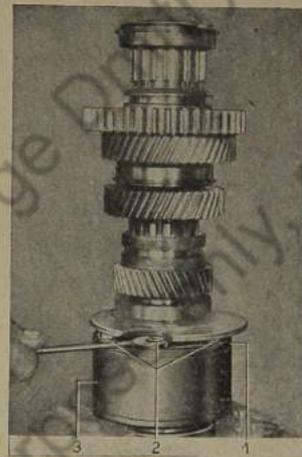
Freilaufsperr an Hauptwelle anschrauben
